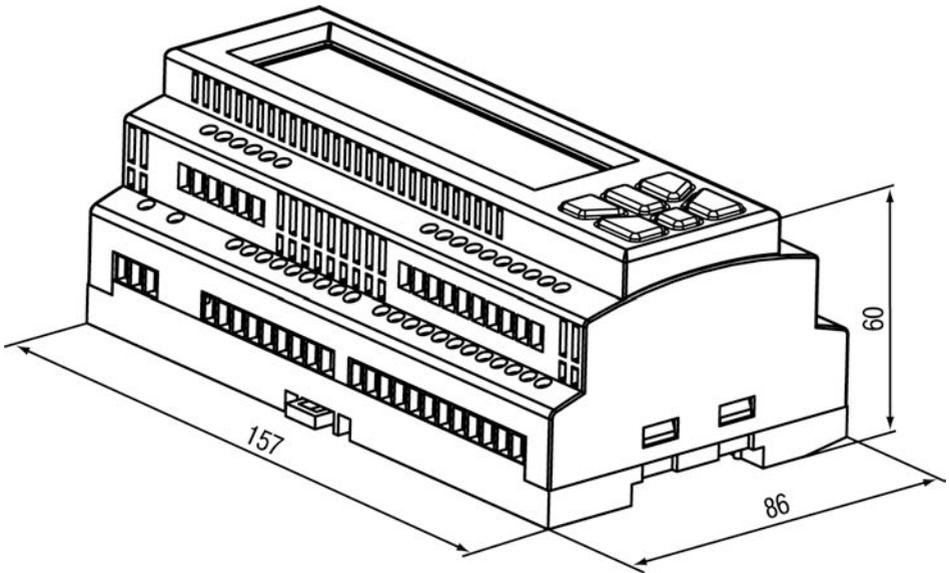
Корпус для крепления на DIN-рейку 35 мм
